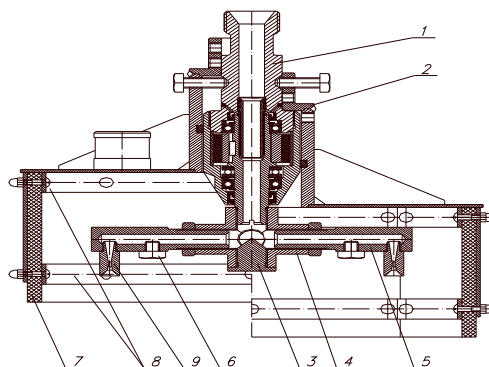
Общее устройство для демаркировки дорожной разметки гидродинамическим методом с применением кавитации: 1 – магнитная насадка; 2 – камера; 3 – заглушка; 4 – головка; 5 – водовод; 6 – пробка; 7 – юбка; 8 – полоса; 9 – кавитатор
